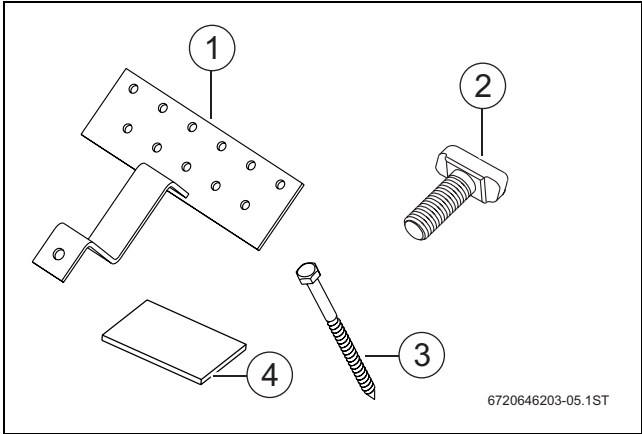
Lieferumfang Haltebügel für Dachziegel (unterschiedliche Haltebügel je nach Dacheindeckung)
